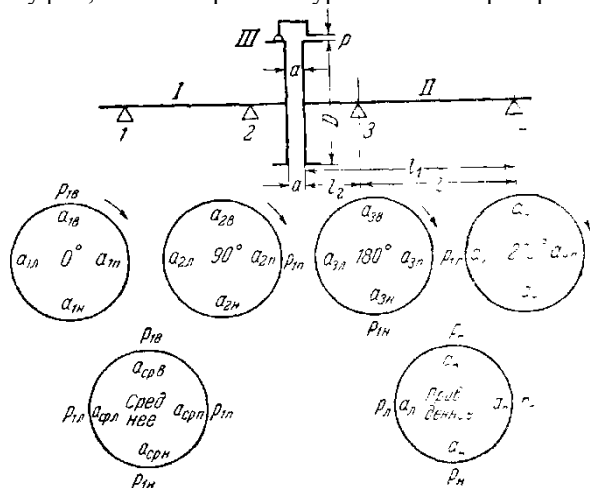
Формуляр центровки роторов по муфтам. I — ротор турбины; II — ротор генератора; III — скоба на роторе турбины.
